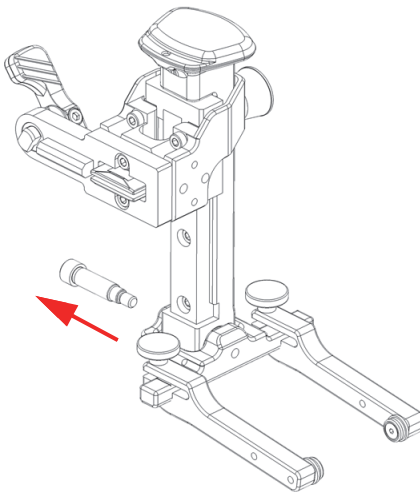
Schraube vom Schwenkträger des Gabelstücks entfernen
